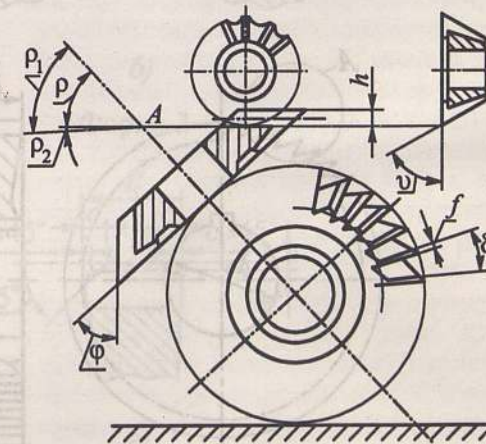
Схема фрезерования зубьев угловой фрезы
